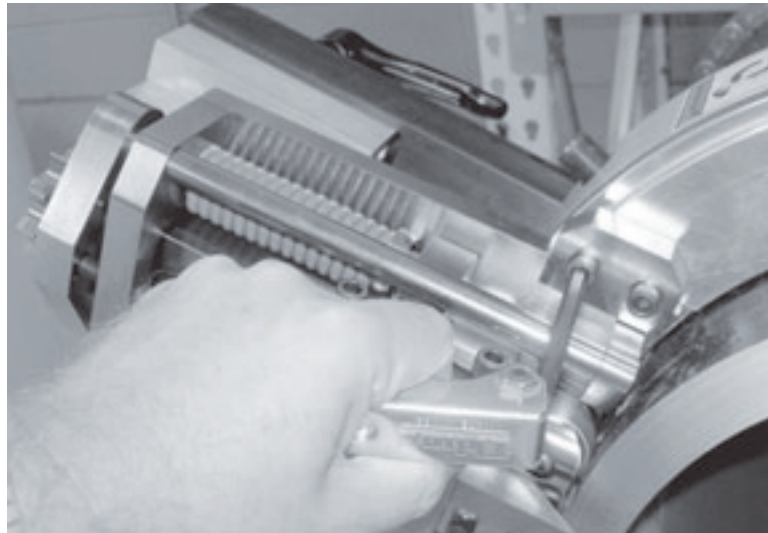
Desserrez les vis des brides de fixation pour déposer les plateaux.
